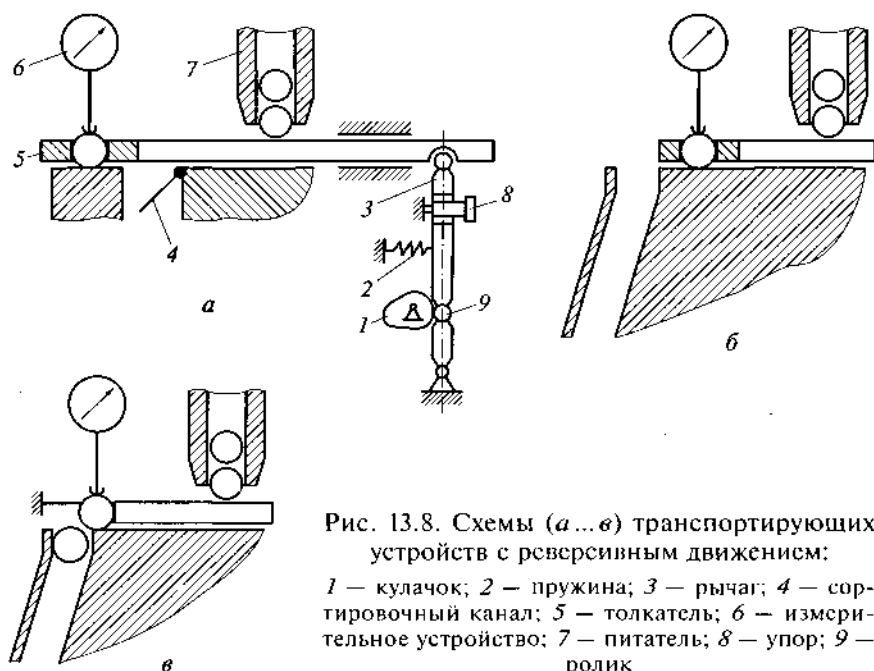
Схемы (а...в) транспортирующих устройств с реверсивным движением:
